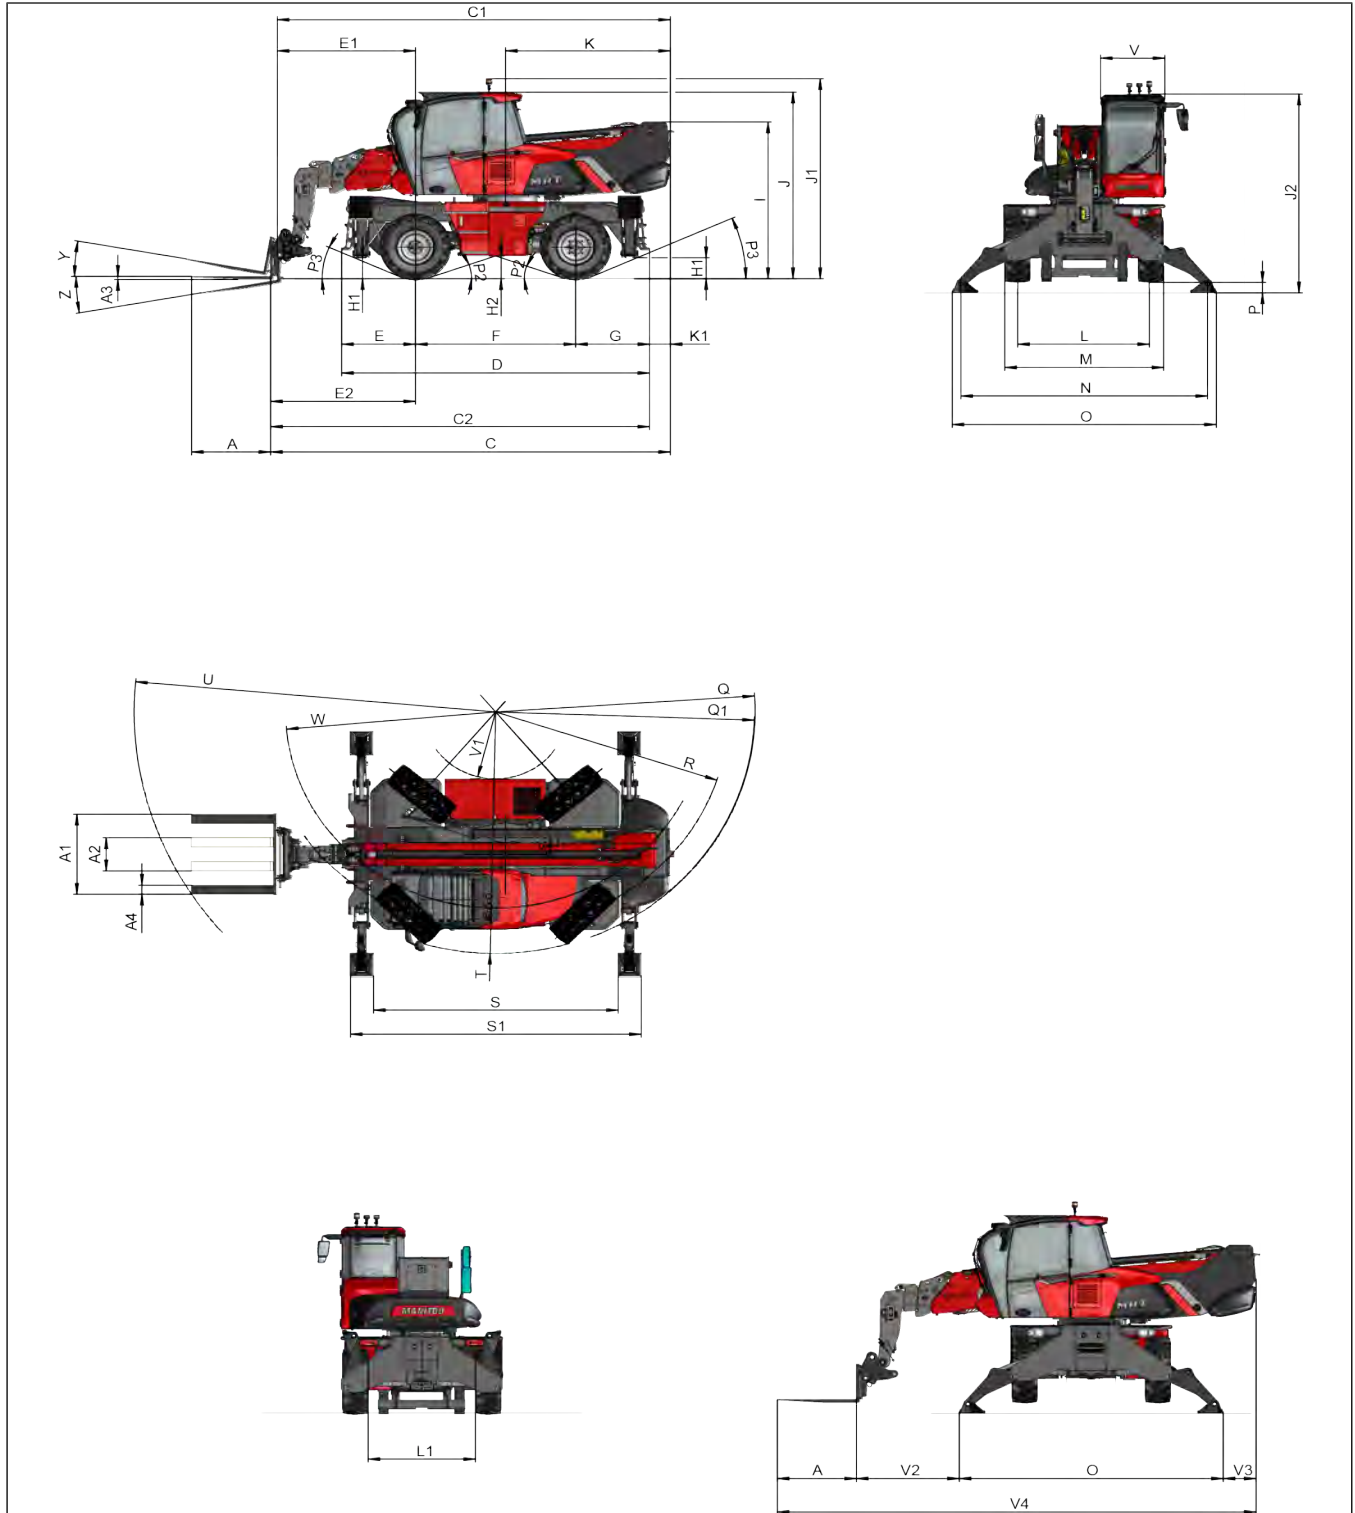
Dimensions (vue latérale, vue de face et vue de dessus)
